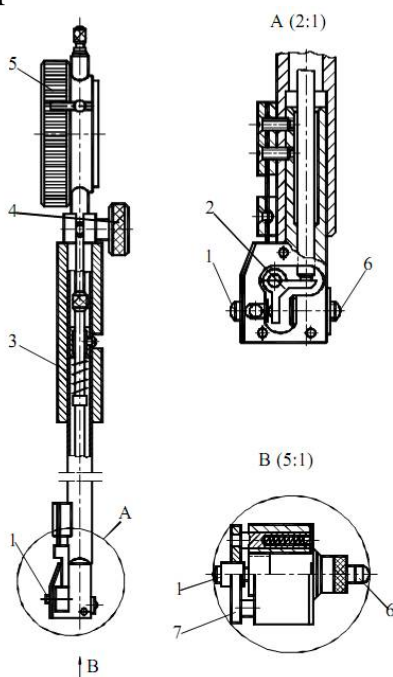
Индикаторный нутромер: 1 – подвижный наконечник; 2 – клинорычажный механизм; 3 – корпус; 4 – зажимной винт; 5 – измерительная головка; 6 – неподвижный сменный наконечник; 7 – центрирующий мостик
